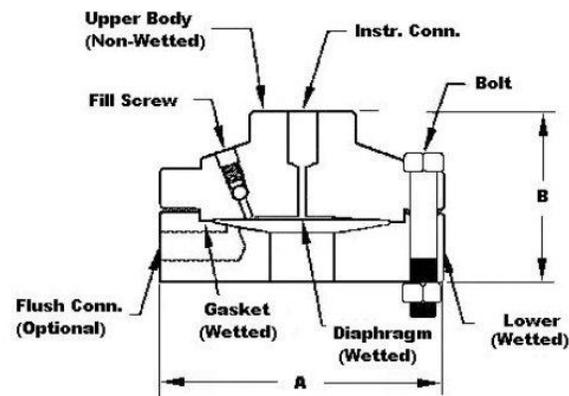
Abmessungen des Druckmittlers (Druckmittler mit Gewinde-Prozessanschluss)
